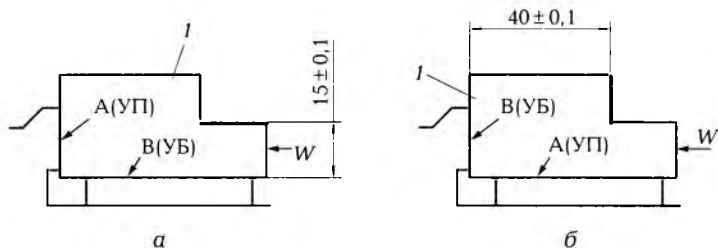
Упорные поверхности и установочные базы для операционного размера $15 \pm 0,1$ (а) и для операционного размера $40 \pm 0,1$ (б):
